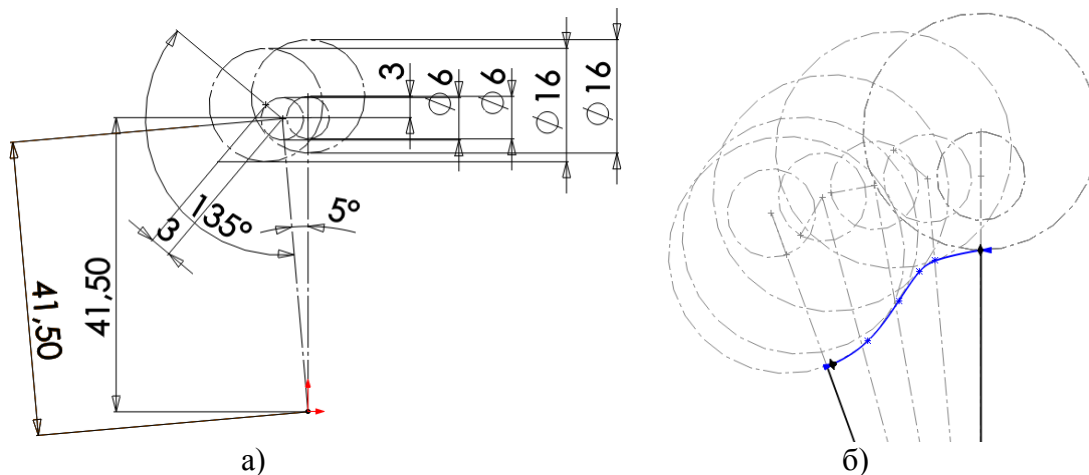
Ескізи SolidWorks для побудови профілю зуба колеса: а - два положення ексцентрикового зуба шестерні; б - утворення половини профілю зуба колеса за допомогою сплайна
